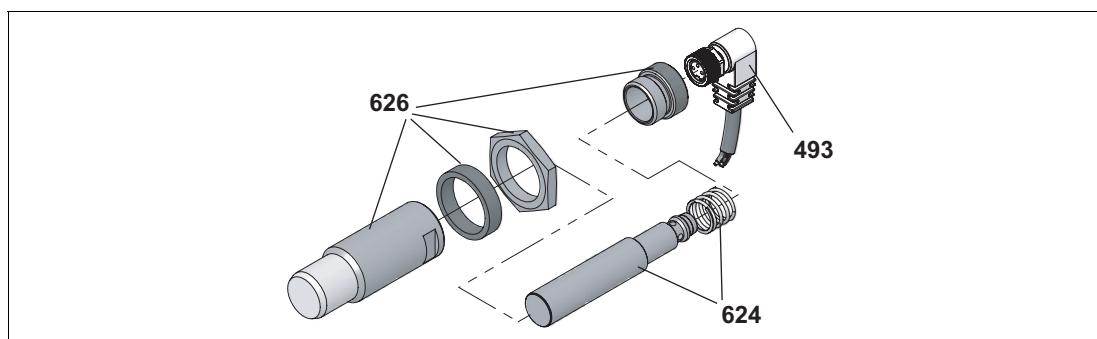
Explosionszeichnung BEG 43D/BEG 46D
